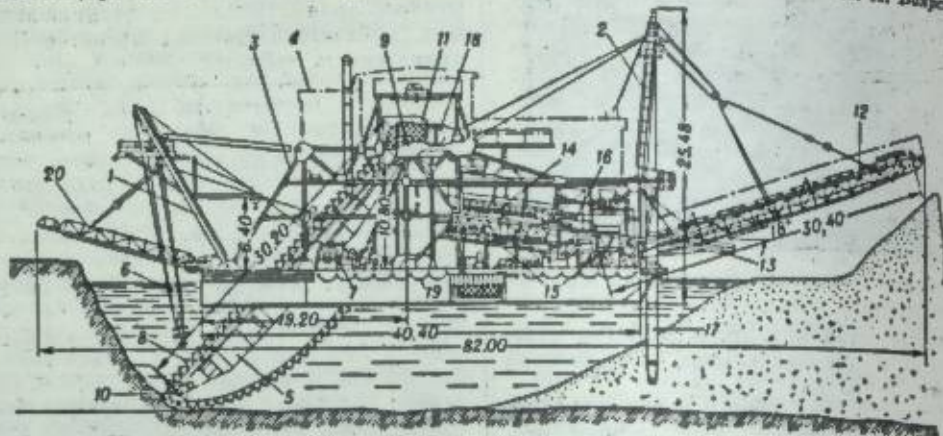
150-литровая драга: 1 — носовая мачта; 2 — кормовая мачта; 3 — суперструктура; 4 — обшивка; 5 — черпаковая рама; 6 — подлисасть; 7 — рамоподъемная лебедка; 8 — черпановая цепь; 9 — верхний черпаковый барабан; 10 — нижний черпановый барабан; 11 — аналочный люк; 12 — отвалообразователь; 13 — эфельная колода; 14 — поперечные шлюзы; 15 — отсадочные машины; 16 — галечный лоток; 17 — свая; 18 — главный привод; 19 — понтон; 20 — береговой мостик.
